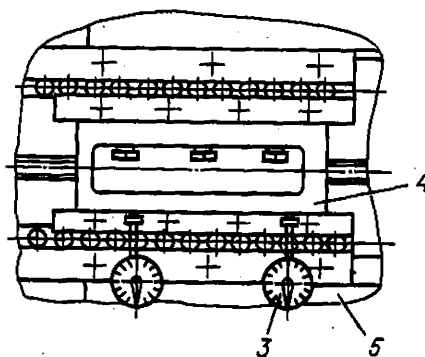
Схема регулировки и контроля натяга в направляющих прибора правки
